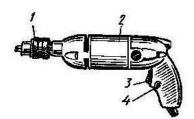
Ручная электрическая сверлильная машина: 1— патров. 2— корпус, 3— курок, 4— выключатель
